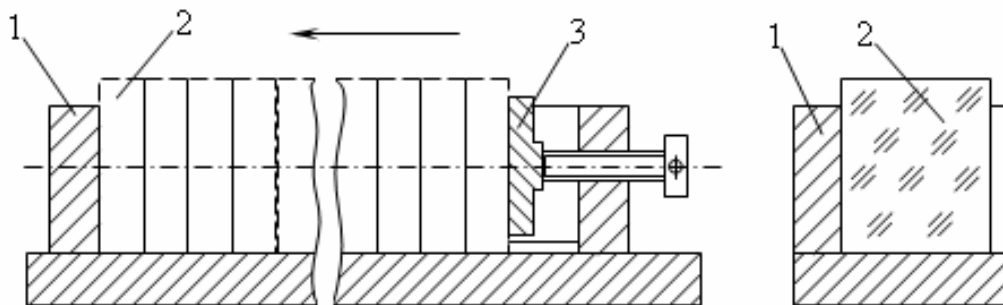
Пристосування для обробки торців заготовок некруглої форми
